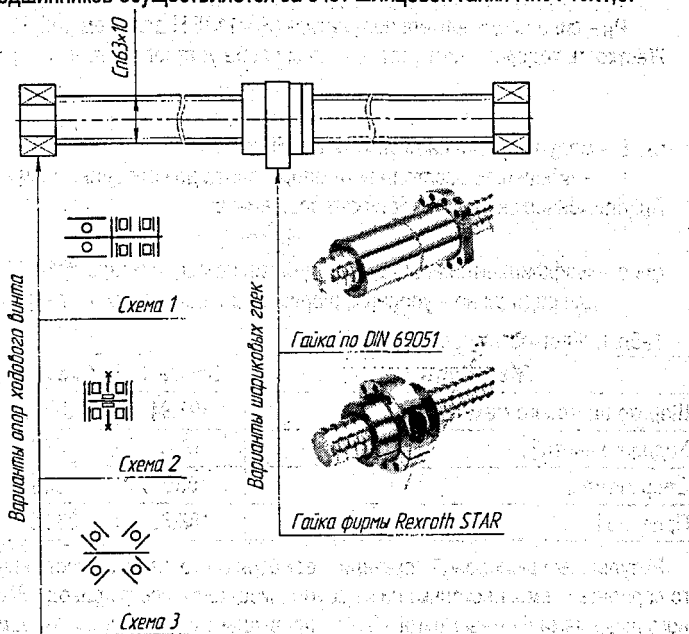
Схемы конструкций тягового устройства токарного станка.
